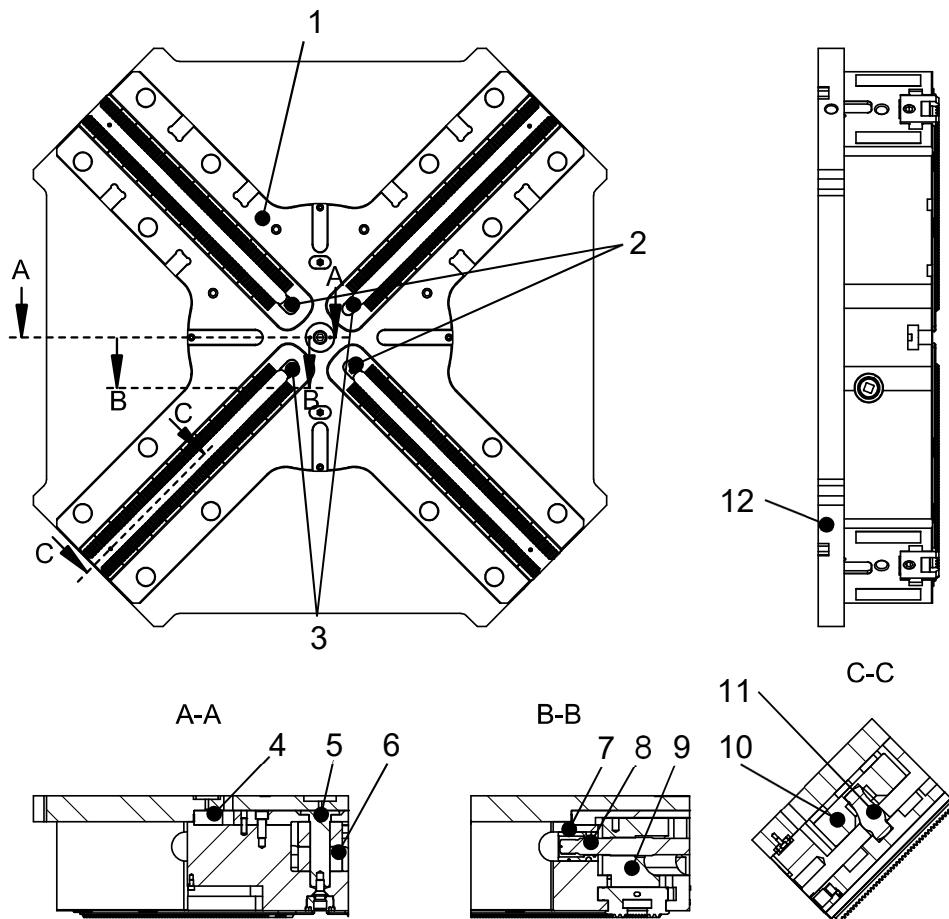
Struttura del mandrino di serraggio INOFlex®
